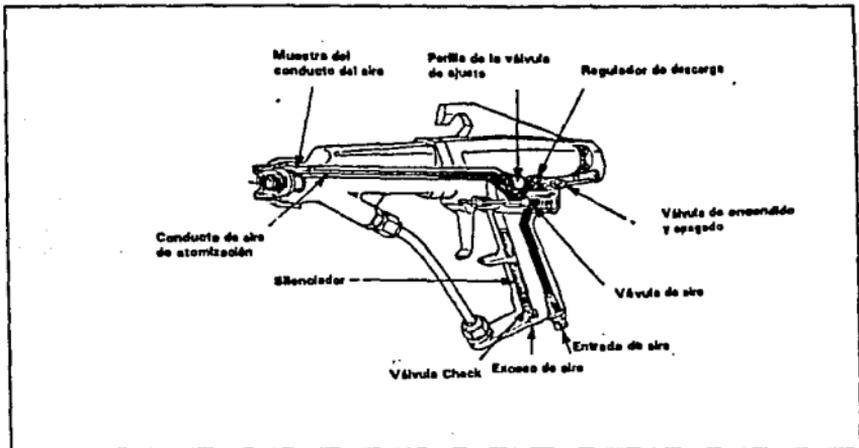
PARTES PRINCIPALES DE UNA PISTOLA ELECTROSTATICA.
